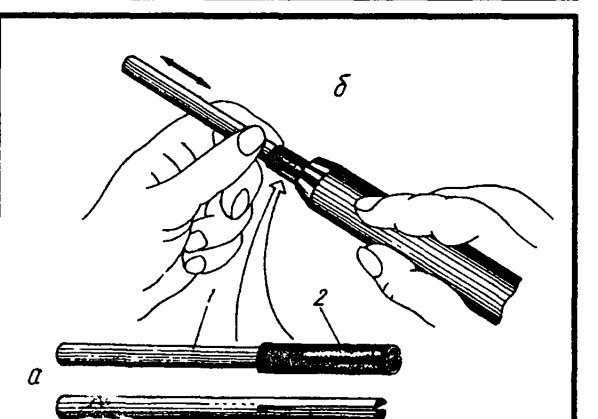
Прутки для правки внутренней части полукруглых резцов:
